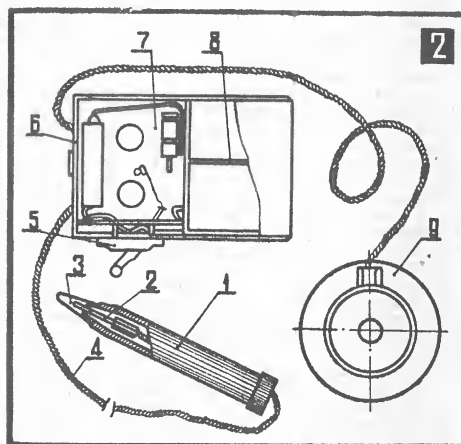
Стетоскоп с отдельным датчиком: 1 — корпус датчика; 2 — пьезокристалл; 3 — защитный наконечник; 4 — провод; 5 — выключатель; 6 — корпус с усилителем и блоком питания; 7 — усилитель; 8 — батареи ФБС; 9 — наушник.
